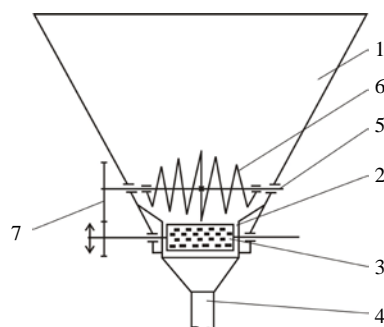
Коническо-винтовой ворошитель-сводообрушитель
